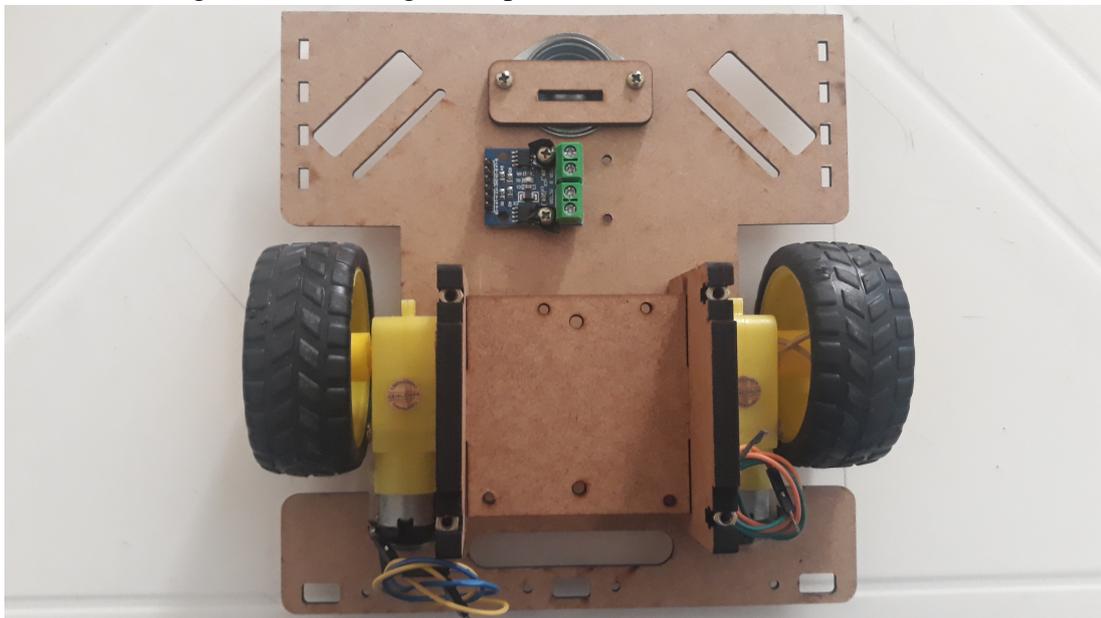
Montagem do segundo conjunto roda motor suporte.
